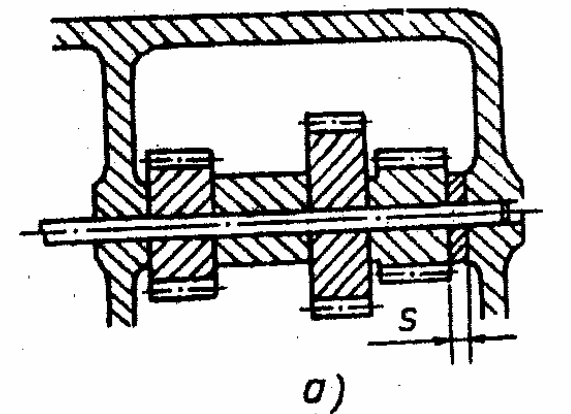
Sơ đồ bố trí dung sai để tính ΔK .
